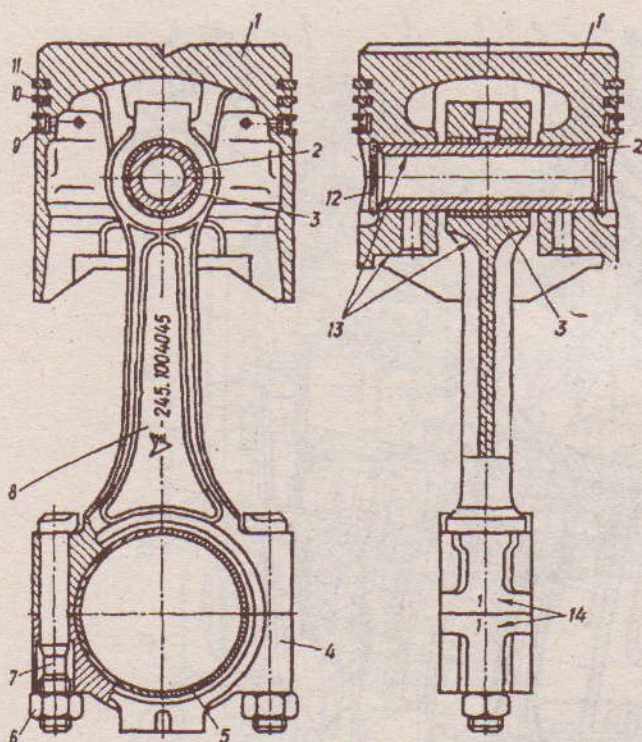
Шатун с поршнем в сборе: 1 - поршень; 2 - поршневой палец, 3 - втулка шатуна; 4 - крышка шатуна; 5 - вкладыши; 6 - гайка болта крышки шатуна; 7 - болт крышки шатуна, 8 - шатун; 9 - маслосъемное кольцо в сборе; 10 и 11 - нижнее и верхнее компрессионные кольца, 12 - стопорное кольцо, 13 - места цветовой маркировки шатуна, бобышки поршня и поршневого пальца; 14 - клеймо номера цилиндра
